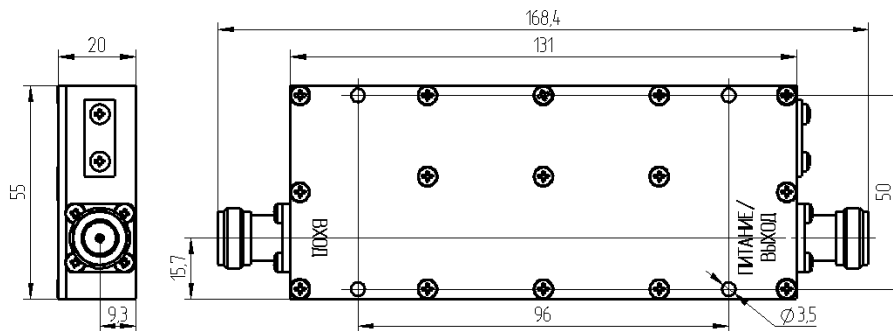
Внешний вид и габаритные размеры МШУ 2025-2110 МГц
